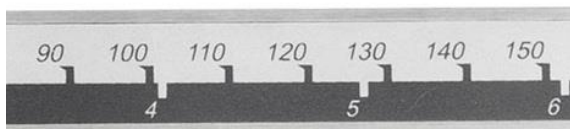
Общий вид исполнений штанги штангенглубиномеров ШГЦ с оцифровкой
